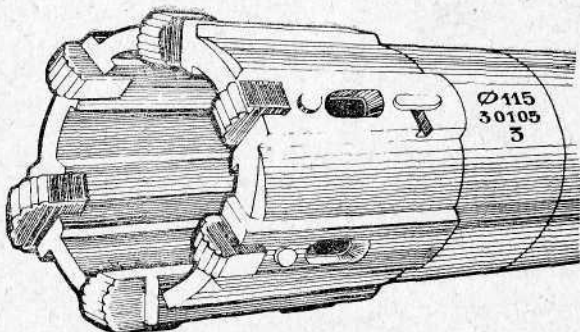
Шестирезцовая головка для глубокого сверления вала турбодолота.
